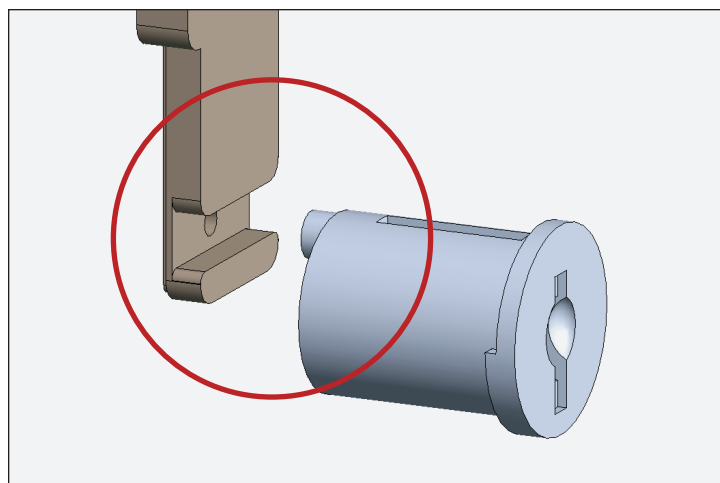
Encoche de la came et goupille du cylindre de la serrure
